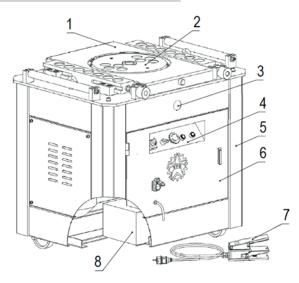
Схема устройства станка для гибки арматуры (ВПК Г-55): 1 — защитная крышка, 2 — поворотный диск, 3 — глазок уровня масла, 4 — панель управления, 5 — корпус станка, 6 — передняя дверца, 7 — ножная педаль, 8 — ящик с ЗИП.
